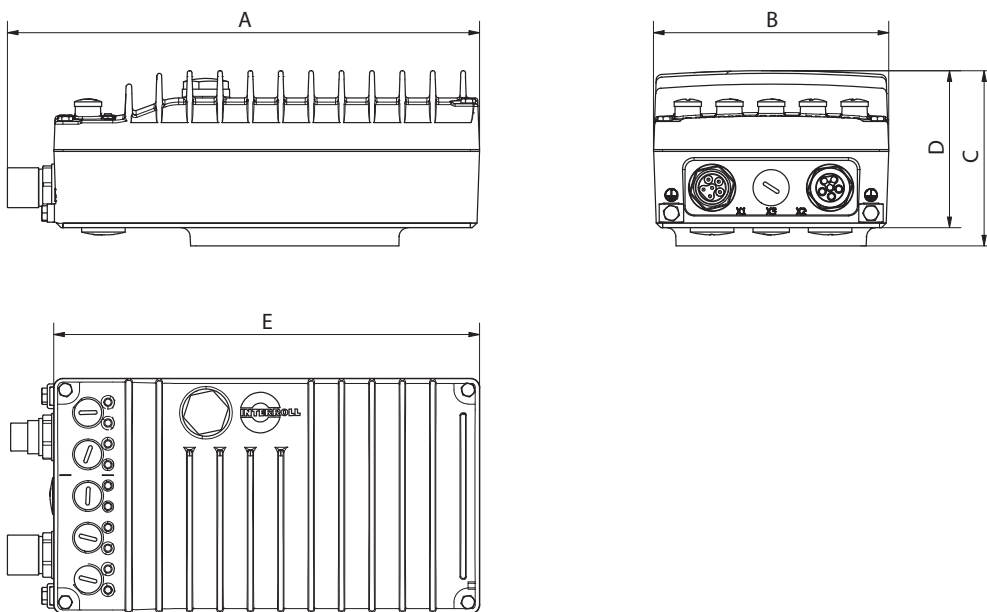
, montaggio sul motore, taglia 1 & 2
